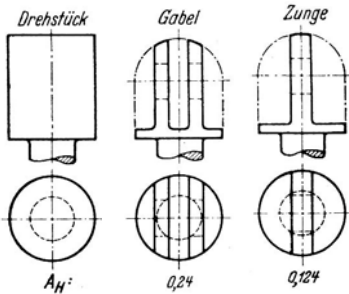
Aus einer Rundstange gefertigte Gabel- und Zungenbolzen.
